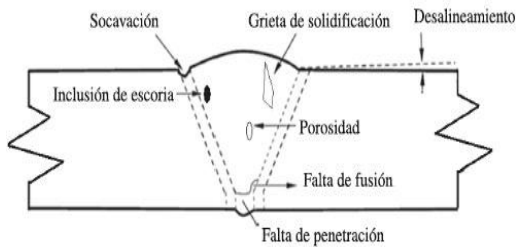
Imperfecciones de soldadura en juntas a tope. Fuente: Maddox (1994).
